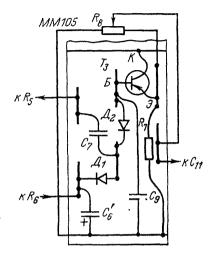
Монтажная схема детектора и входного эмиттерного повторителя УНЧ.
